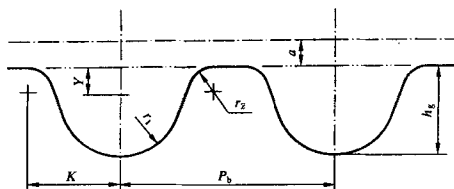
加工 ZH 型带轮的齿条刀具(齿数 27~52)
